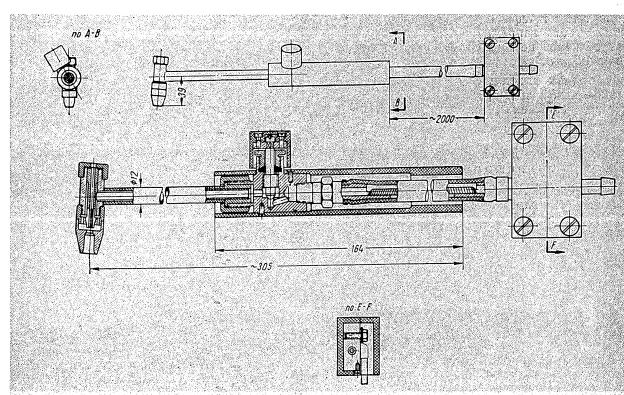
Сварочная горелка малого габарита для ручной сварки в среде аргона
